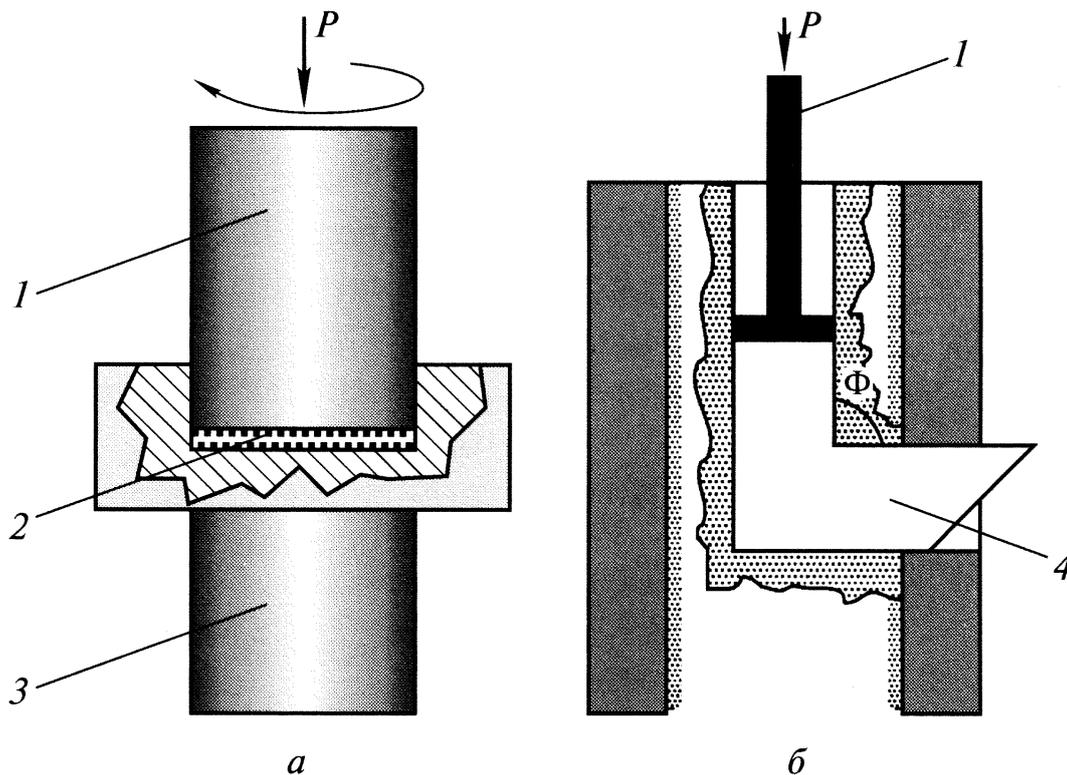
Схема методов интенсивной пластической деформации: а- метод кручения под высоким давлением, б- метод равноканального углового прессования, 1- пуансон, 2- образец, 3- суппорт, 4- заготовка [2].
